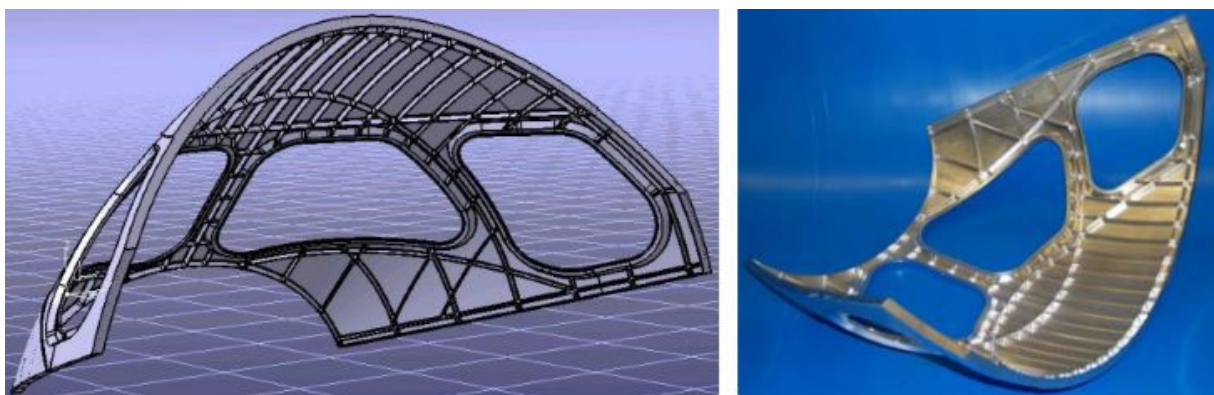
Structure du cockpit d'une tôle formée par explosion, composée d'aluminium 2139
